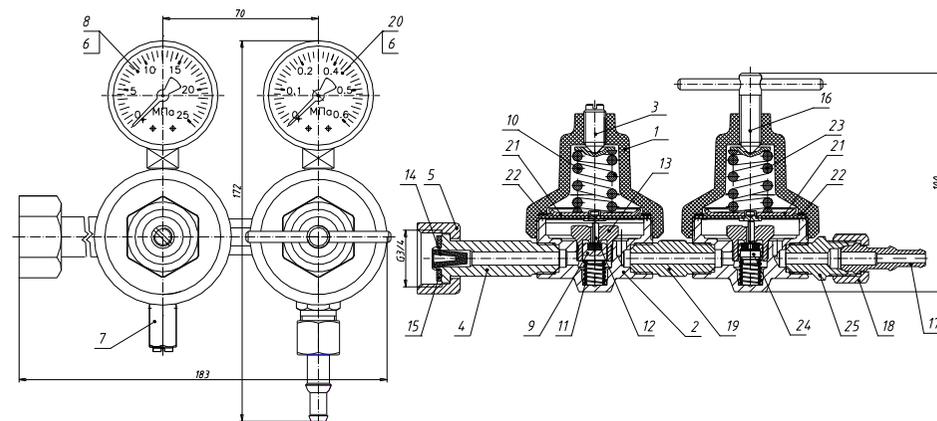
Редуктор баллонный газовый двухступенчатый:
